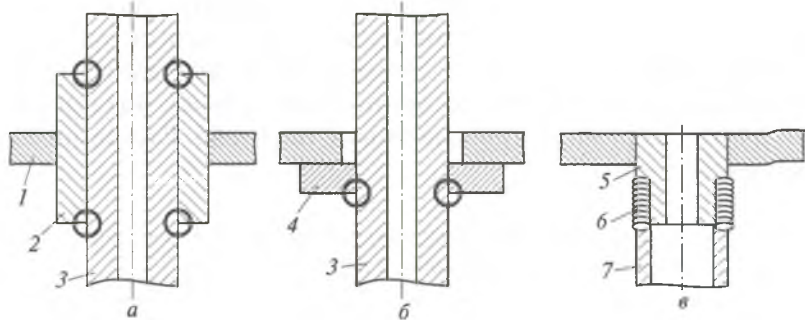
Схема соединения стальных конструкций с медными и медно-никелевыми трубами:
